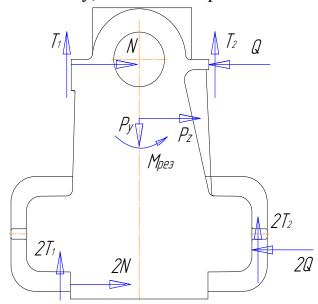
Схема заготовки под действием внешней нагрузки
